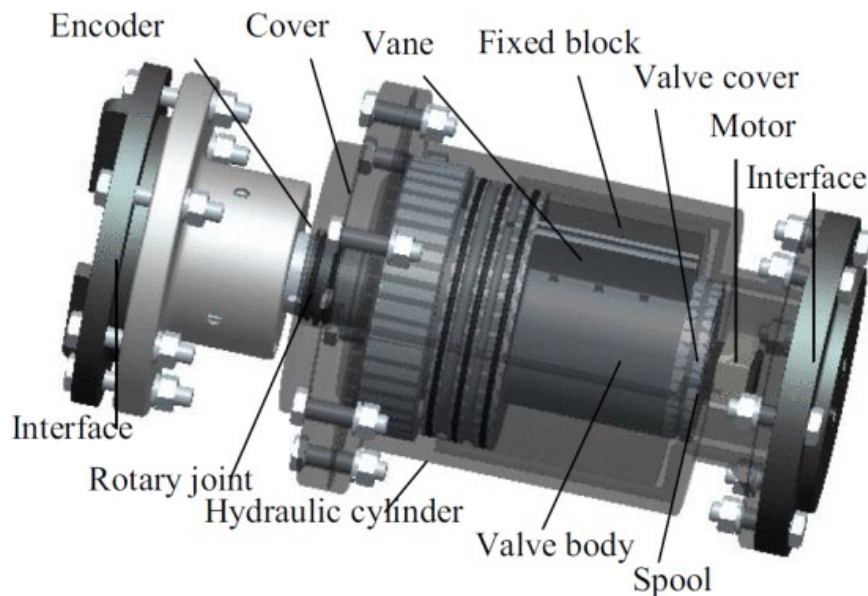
Struttura del giunto idraulico rotativo [9]
